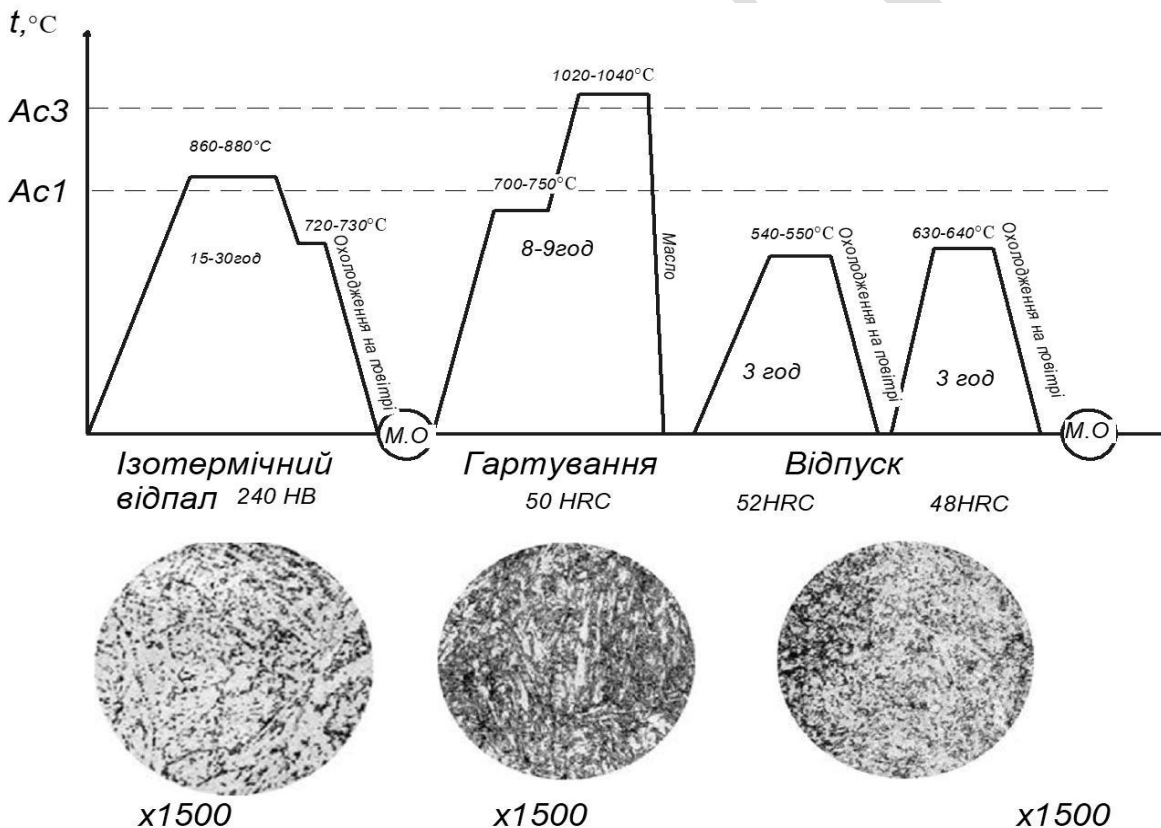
Схема термічної обробки деталі «матриця» зі сталі 4X5МФ1С.
